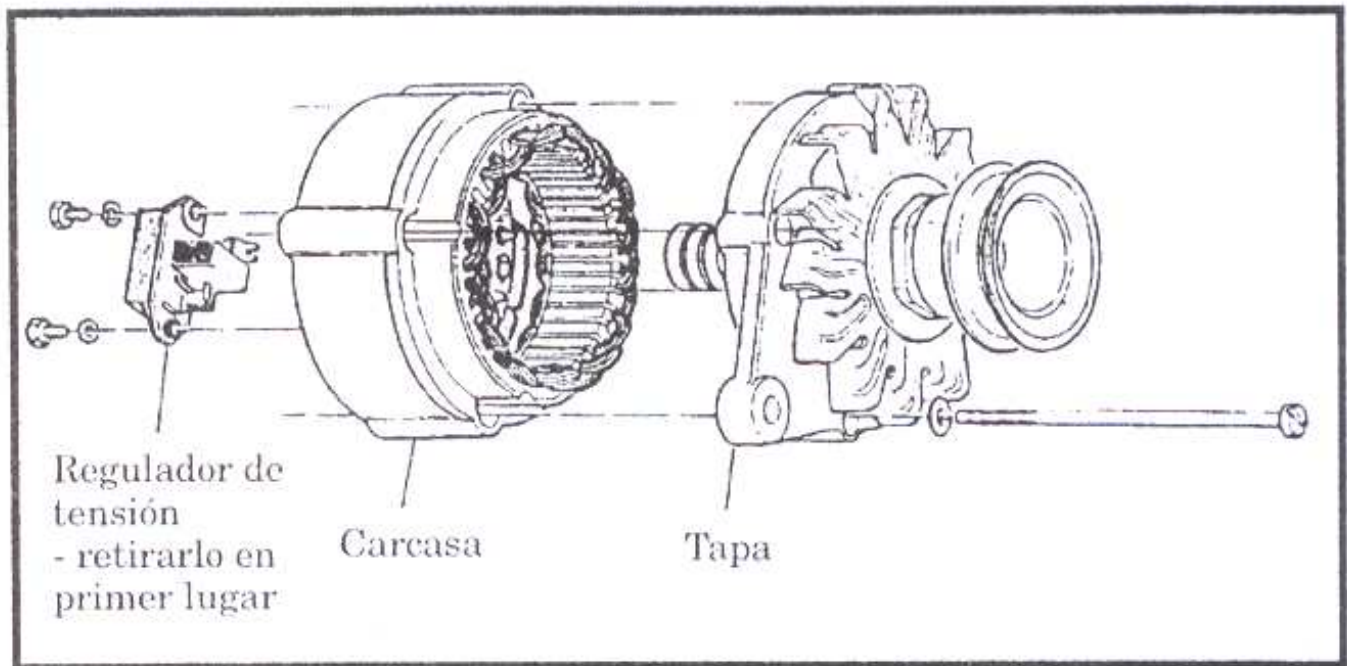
Desmontaje de la parte trasera del alternador.
